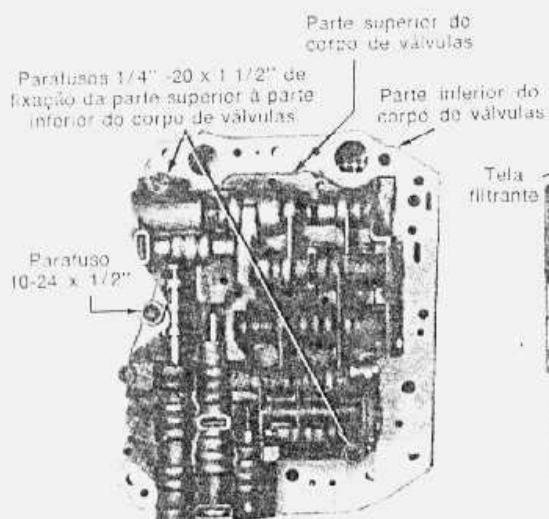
parafusos de montagem das partes do corpo de válvulas
